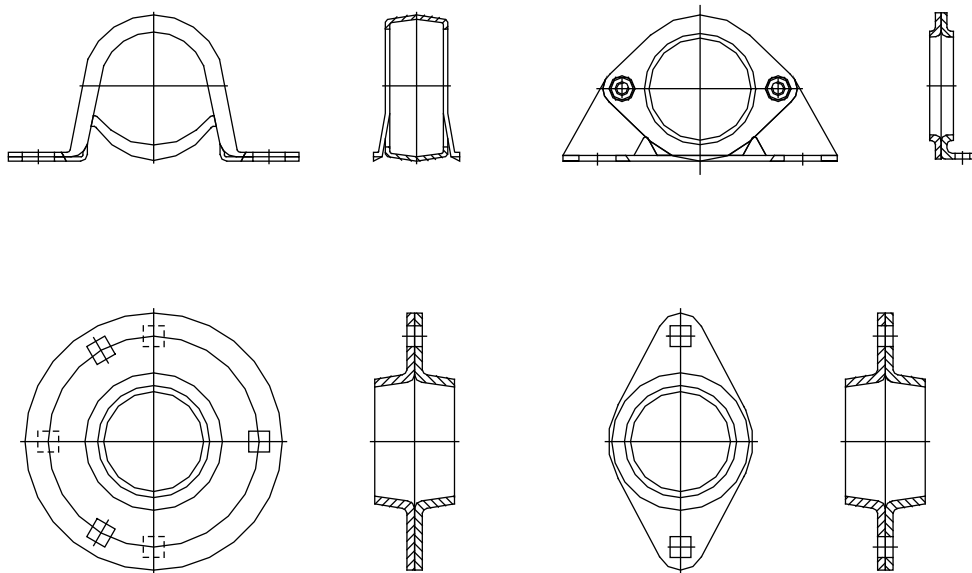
стандартные типы корпусов NKE из штампованной стали
